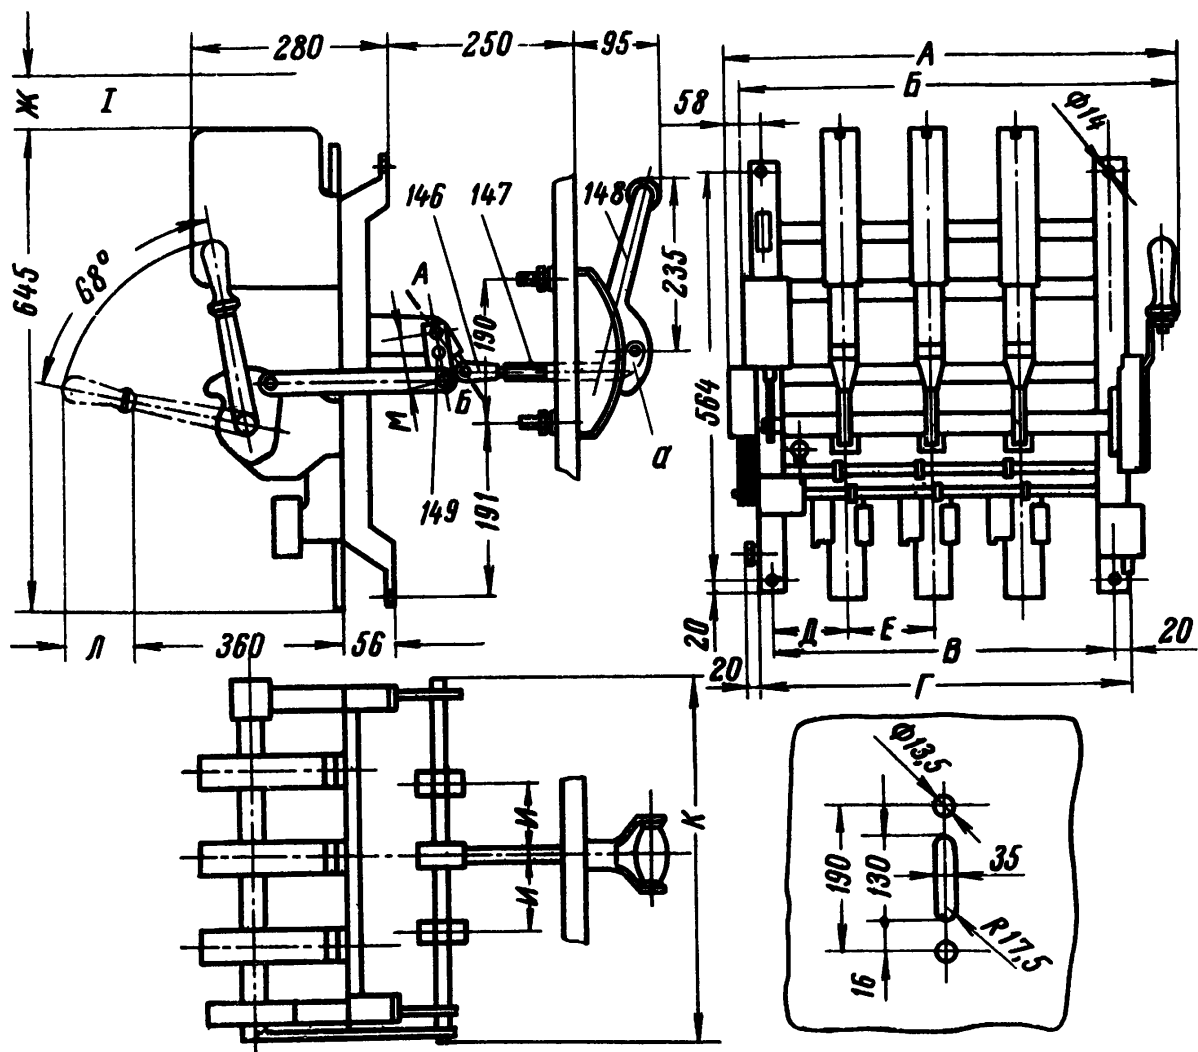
Габаритно-установочные размеры стационарных выключателей с рукояткой и рычажным приводом:
